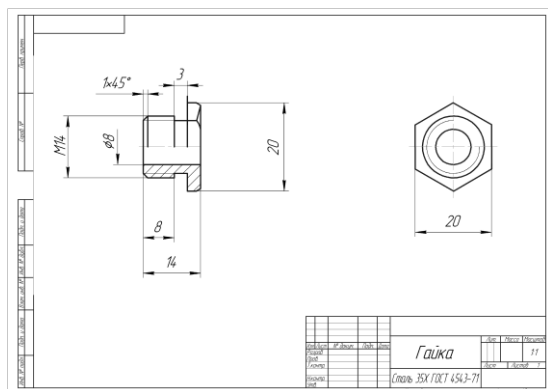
Уточненный рабочий чертеж детали «Гайка»
